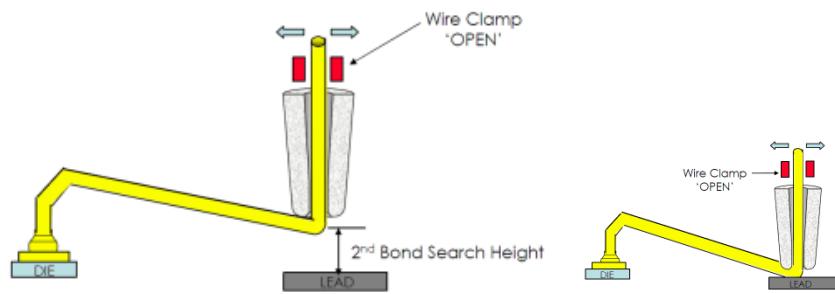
Схема формирования 2-го сварного соединения «клип»
